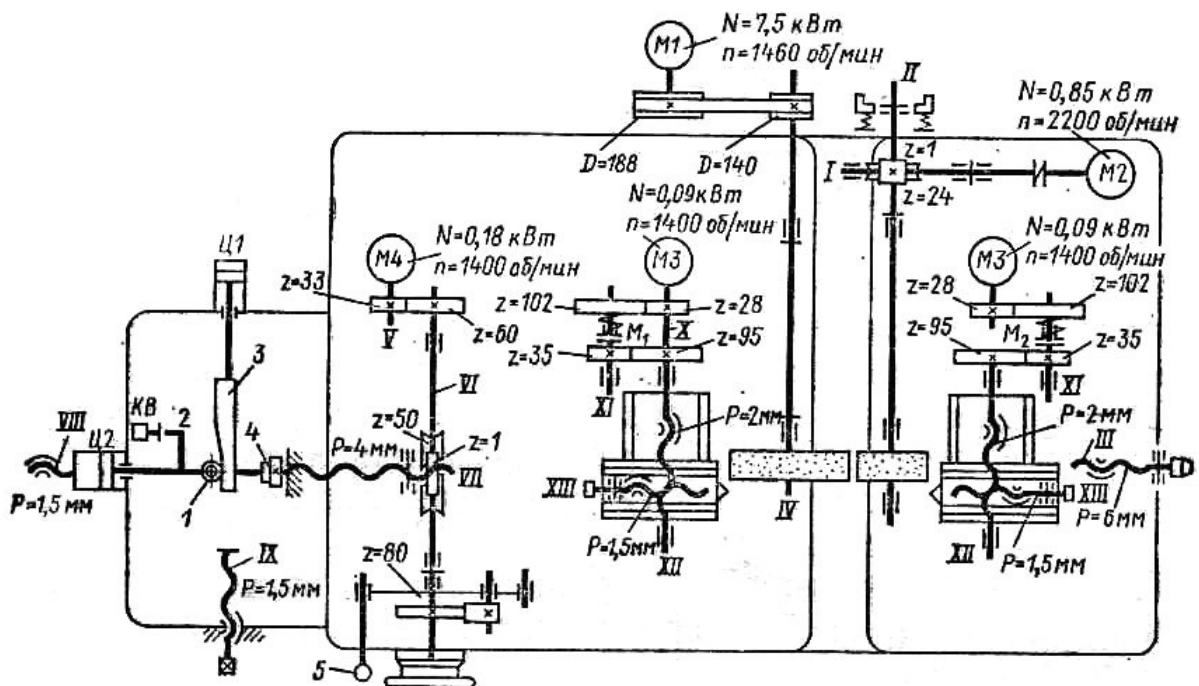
Кинематическая схема бесцентрово-шлифовального станка модели 3М182
